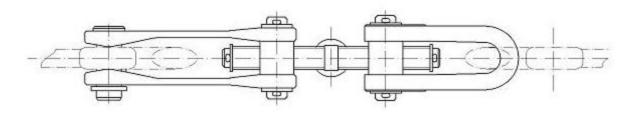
Винтовая стяжка с шарнирной рукояткой в форме шара
